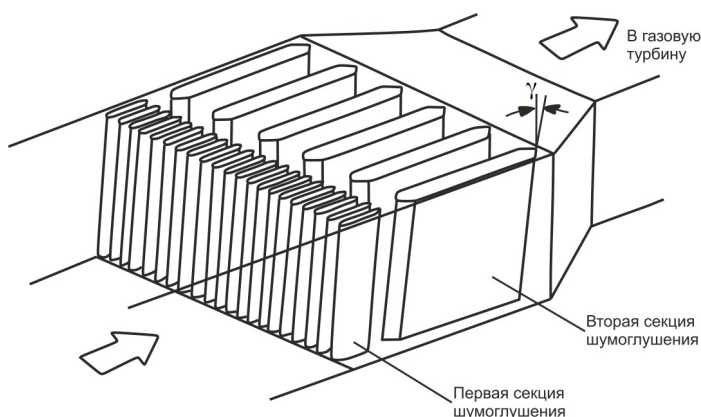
Модернизированный пластинчатый глушитель ВЗУ ГТУ
